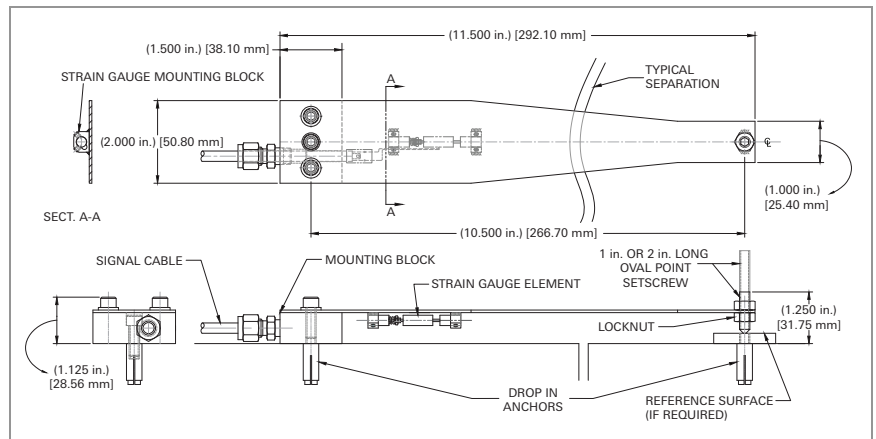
Plano del medidor de grietas de cuerda vibrante de bajo perfil Modelo 4420-3
